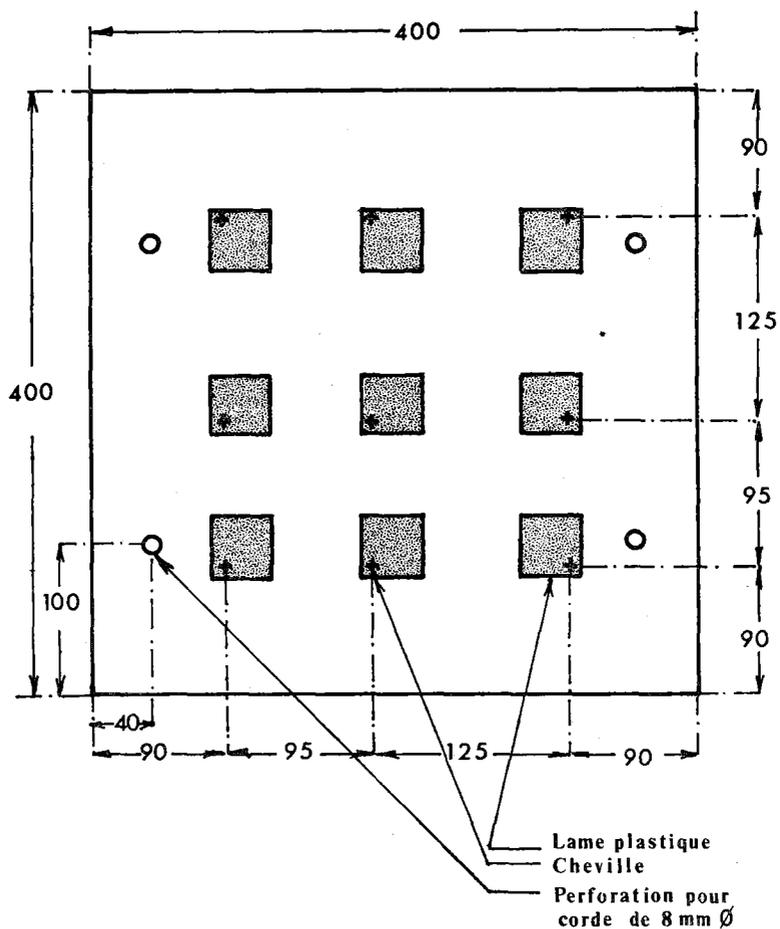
Schéma des dalles d'implantation utilisées à Djibouti.
